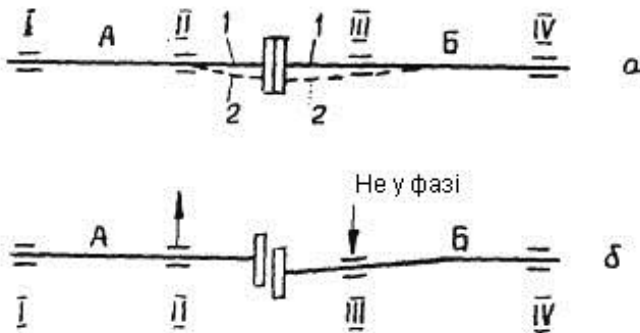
Зсув одного з підшипників агрегата:
